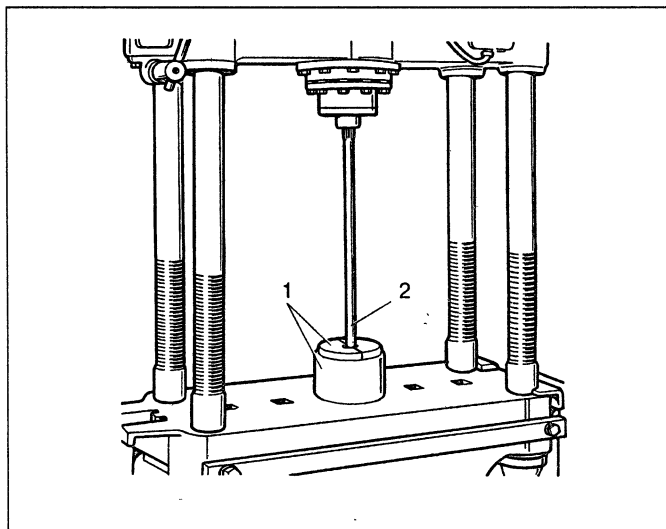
Выпрессовка запорного кольца подшипника полуоси: 1 – приспособление; 2 – полуось
